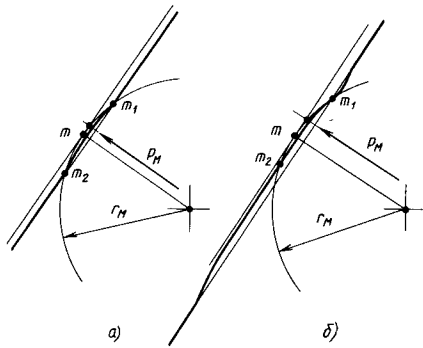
Схема смятия поверхностей контакта заготовки и матрицы:
